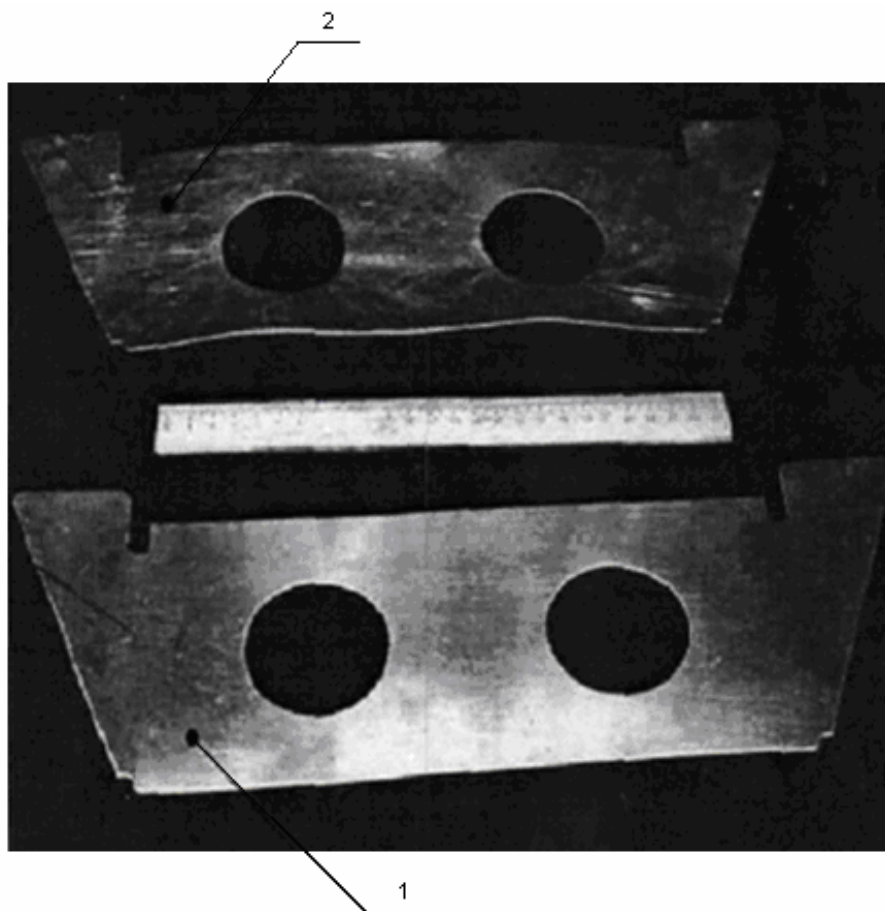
Детали из АМг6М толщиной  $S=0,5$  мм, вырезанные полиуретаном полукоткрытым способом: 1- со смазкой; 2- без смазки.
